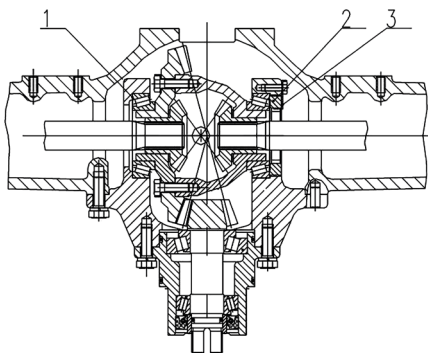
Регулировка подшипника корпуса дифференциала
